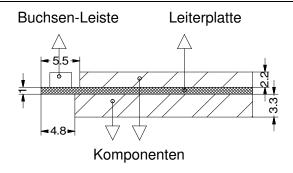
Decoder mit Buchsen-Leiste, Seitenansicht
